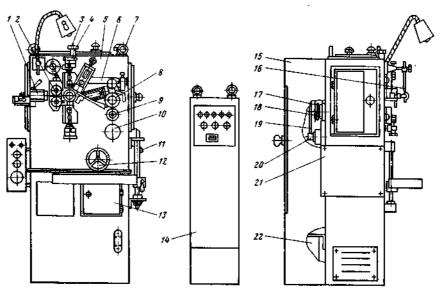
Автомат для холодной навивки пружин из проволоки диаметром 0,2-0,8 мм (мод. AA5109): I — устройство правильное; 2 — механизм подачи; 3, 6 — механизмы образования диаметра; 4 — механизм реза и образования шага; 5 — станина; 7 — механизм привода и корректировки шага; 8 — вал распределительный; 9 — привод механизма реза; 10 — валы приводные; 11 — механизм переключения скоростей; 12 — ручной проворот; 13 — привод; 14 — электрошкаф; 15 — ограждение; 16 — оптическое устройство; 17 — гитара; 18 — вал кривошипный; 19 — механизм кривошипно-коромысловый; 20 вал с обгонными муфтами; 21 — электрооборудование; 22 — система смазки
